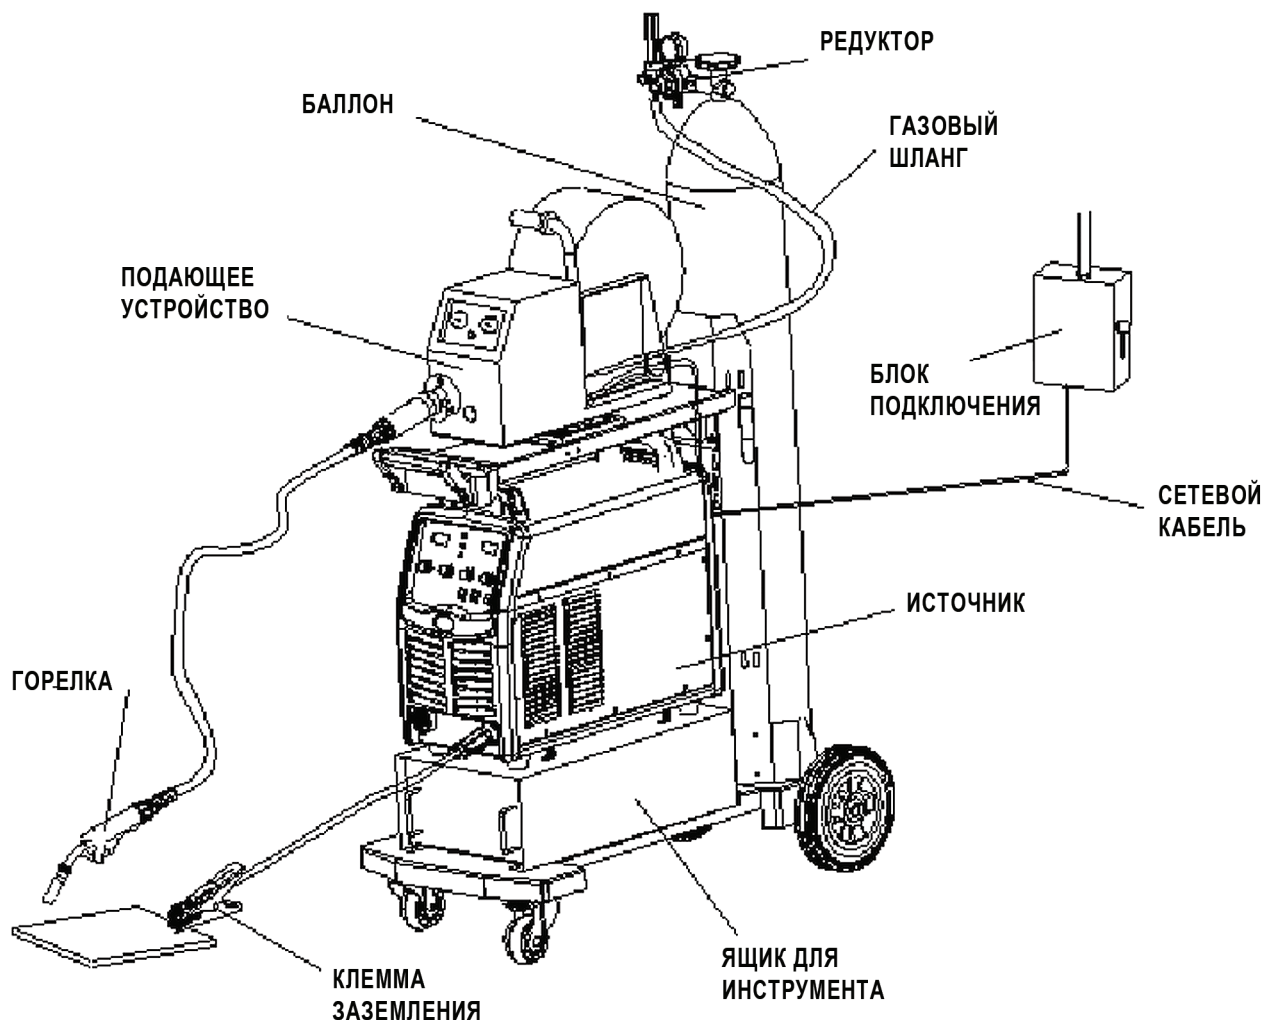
Схема подключения оборудования для механизированной (MIG / MAG) сварки в среде защитных газов.
